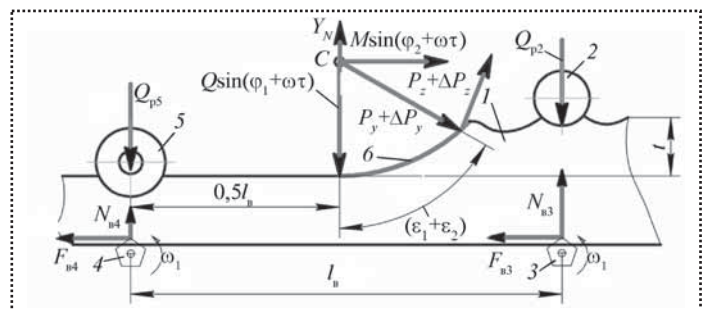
Схема обработки заготовки без дополнительной опоры: 1 – заготовка; 2 – заостренный ролик; 3, 4 – приводные валцы; 5 – фасонный прижимной ролик; 6 – след реза зубом фрезы; Q и M – центробежная сила и инерционный изгибающий момент, обусловленные дисбалансами фрезы; ϕ_1 и ϕ_2 – углы силы Q и момента M соответственно; ω – угловая скорость фрезы; τ – текущее время обработки; Q_{p2} и Q_{p5} – силы прижатия заготовки роликами 2 и 5; $P_y + \Delta P_y$ – радиальная составляющая силы резания; $P_z + \Delta P_z$ – главная составляющая силы резания; N_{n3} и N_{n4} – нормальные реакции валцов 3 и 4; F_{b3} и F_{b4} – тяговые усилия, создаваемые валцами 3 и 4; ω_1 – угловая скорость валцов 3 и 4; l_n – межосевое расстояние валцов; $(\epsilon_1 + \epsilon_2)$ – угол контакта фрезы с заготовкой; t – глубина резания
